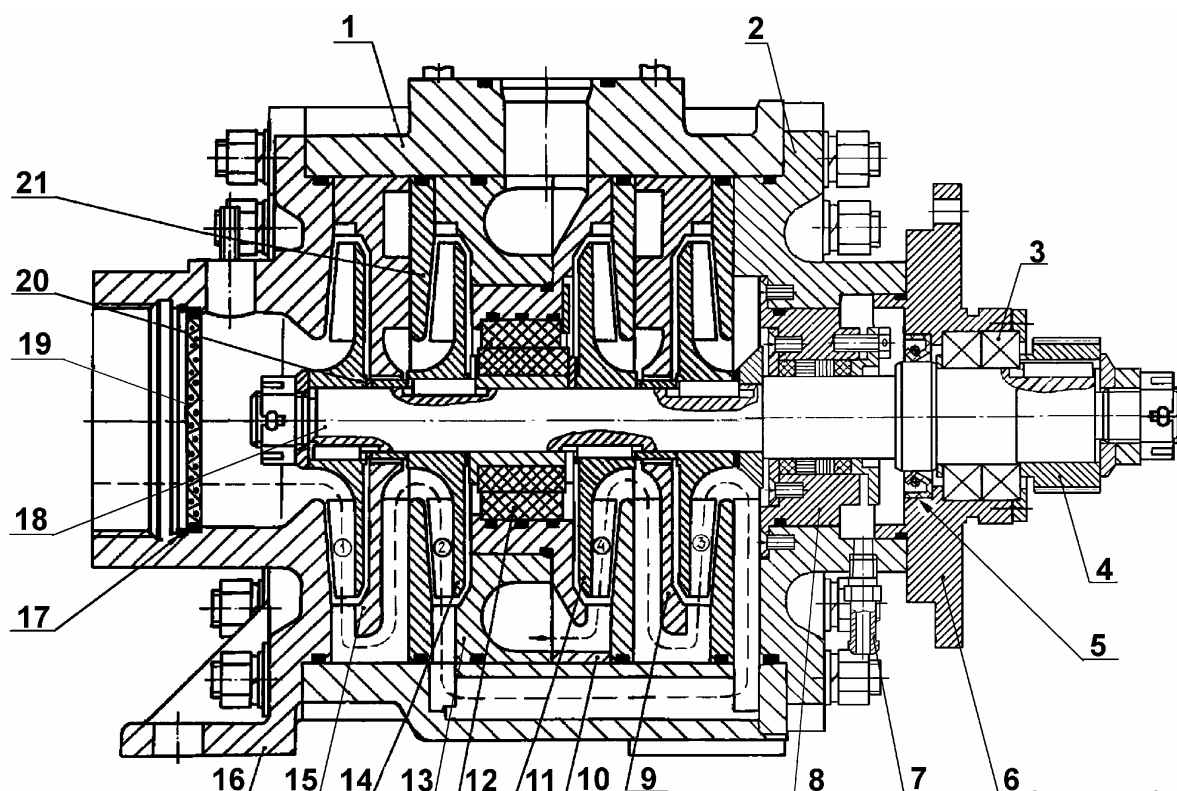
Насос центробежный: 1 - корпус насоса; 2 – задняя крышка; 3 - шарикоподшипник; 4 – колесо цилиндрическое косозубое; 5 – манжета; 6 – корпус задней опоры; 7 – штуцер дренажного отверстия; 8 – сальниковое уплотнение вала; 9,10,13,15 - направляющий аппарат; 11,14 - рабочее колесо; 12 - опора скольжения; 16 - передняя крышка; 17 – стопорное кольцо; 18 - вал; 19 - сетка защитная диск; 20 - прокладка; 21 - диск.
